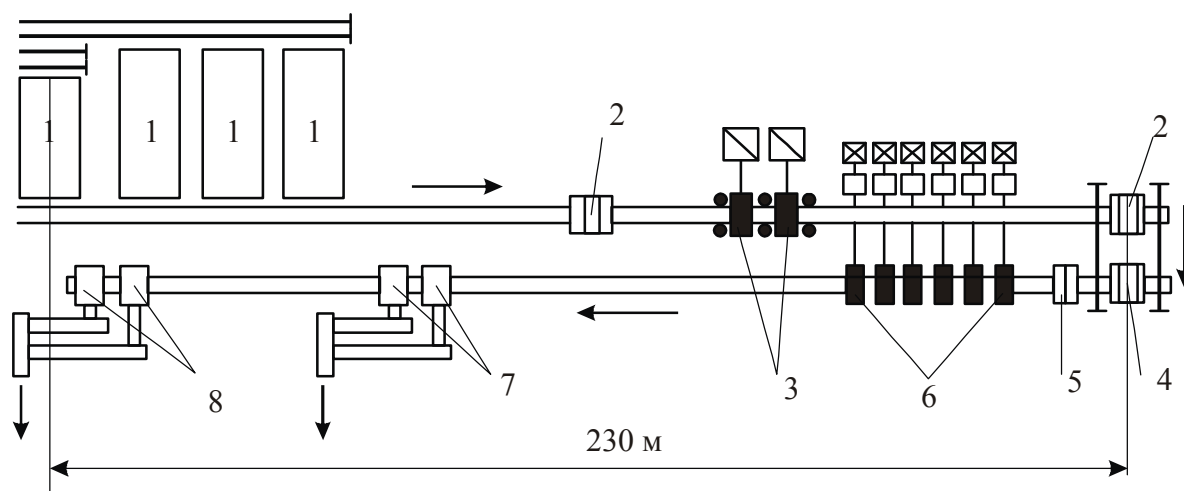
Схема зворотньо-напівбезперервного широкоштабового стану:
